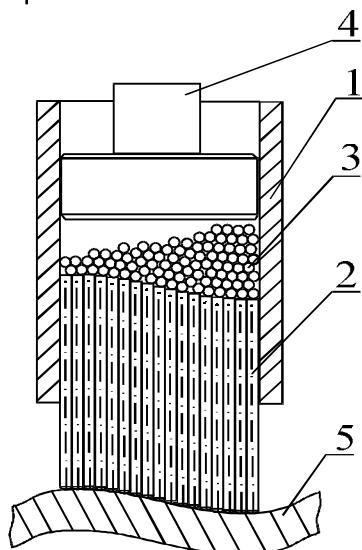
Схема многоконтактного виброударного инструмента ШСУ: 1 — корпус; 2 — стержни; 3 — замкнутый объём с закалёнными стальными шарами; 4 — ударник; 5 — деталь
